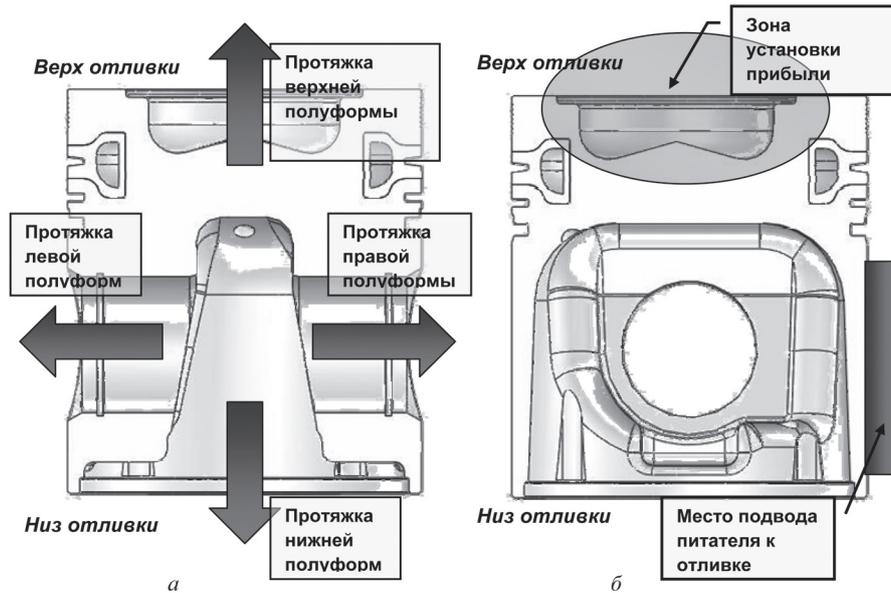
Положение отливки в форме и схема разборки кокиля: а – сечение отливки вдоль отверстий под поршневой палец; б – сечение отливки перпендикулярно отверстию под поршневой палец
